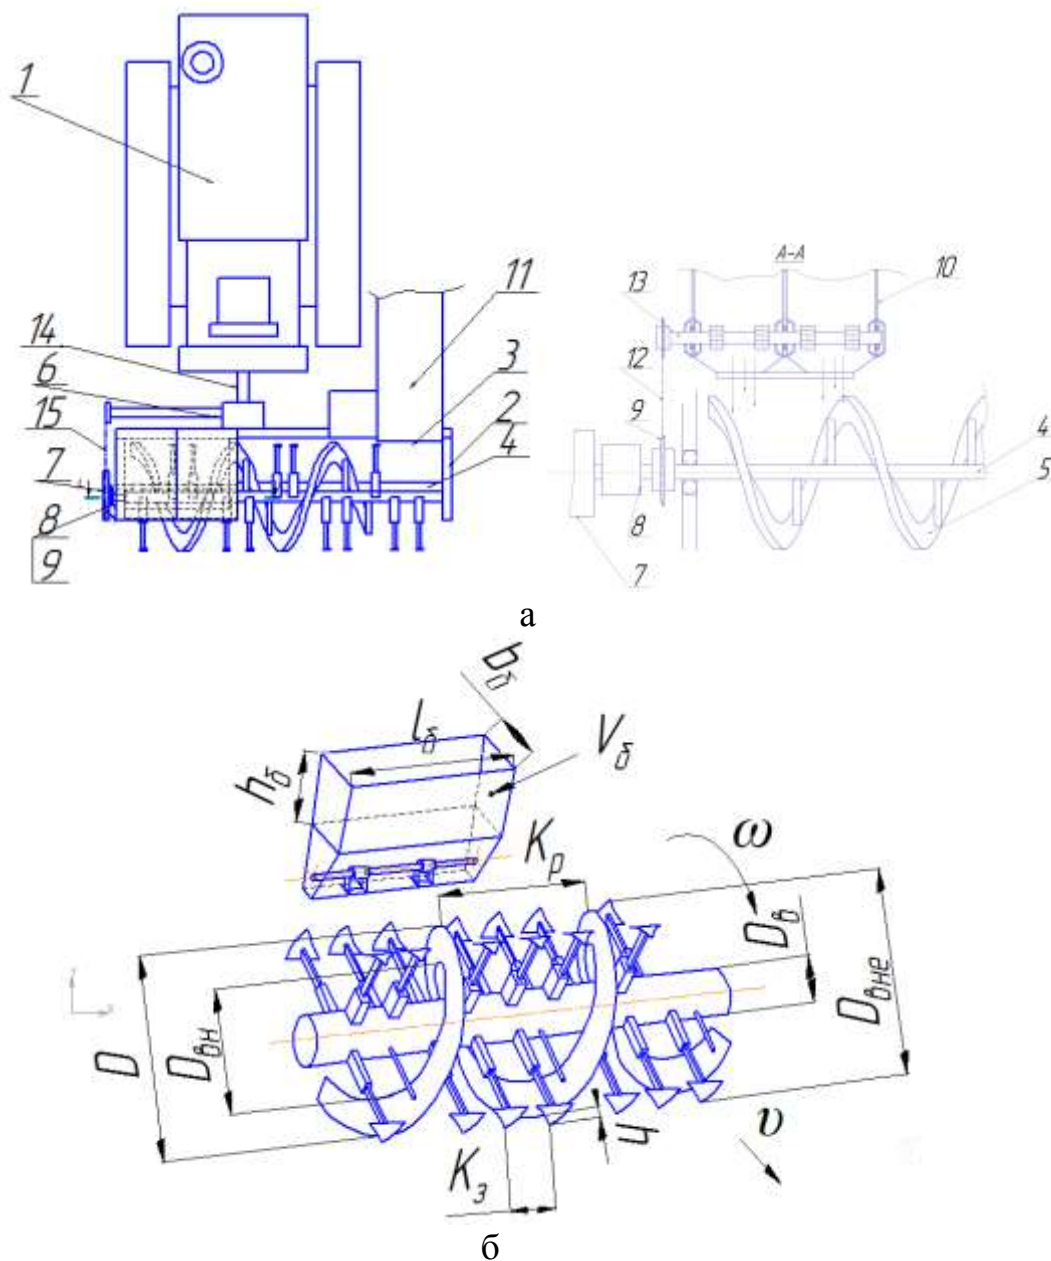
Схема предлагаемого погрузчика-смесителя (а) органоминерального компоста и его рабочих органов (б): 1 – базовая машина; 2 – рама; 3 – отгрузное окно; 4 – вал; 5 – ленточный шнек; 6 – редуктор; 7 – цепь; 8 – муфта; 9 – звездочка; 10 – бункер-дозатор; 11 – отгрузочный транспортер; 12 – цепь; 13 – дозирующий вал; 14 – вал отбора мощности; 15 – цепь
